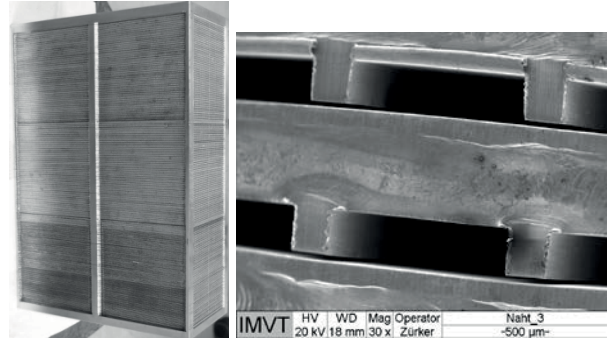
Links: Umfangsschweißen an einem Multilagen-Blechstapel (Format 200x100mm) mit Mikrostrukturen. Blechdicke 0,63 bzw. 1mm. Rechts: Detail.
